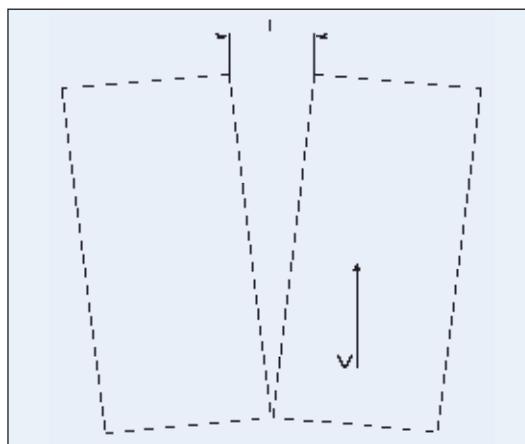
Метод сварки листов с предварительным раскрытием кромок: L — величина раскрытия 10–20 мм на 1 м длины шва; V — направление сварки
